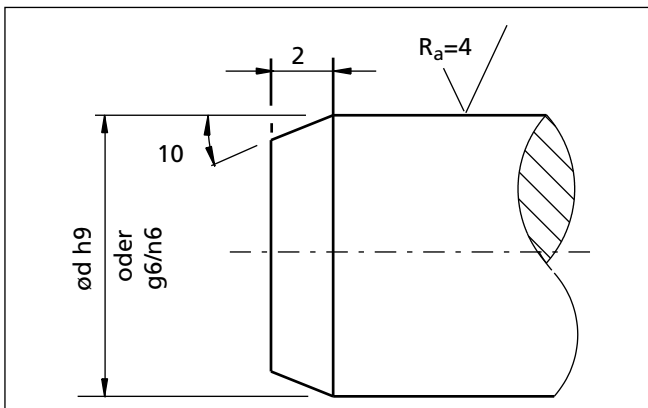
Durchmesser tolerance, Oberflächenrauheit und Kantenfäse der Welle
